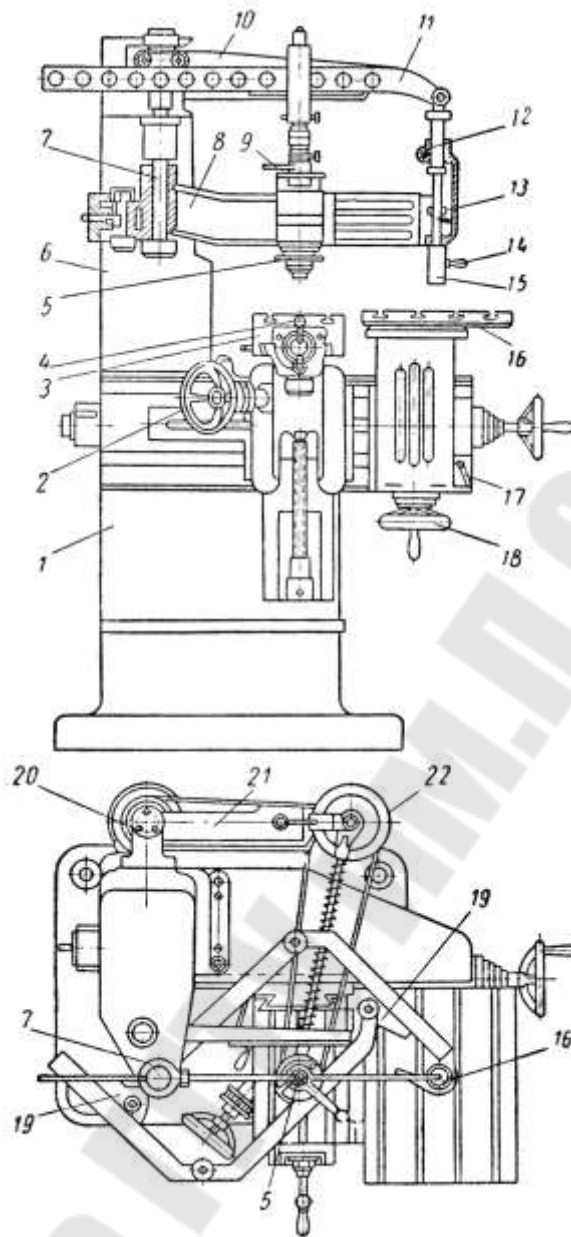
Общий вид копировально-фрезерного станка модели 6461:
